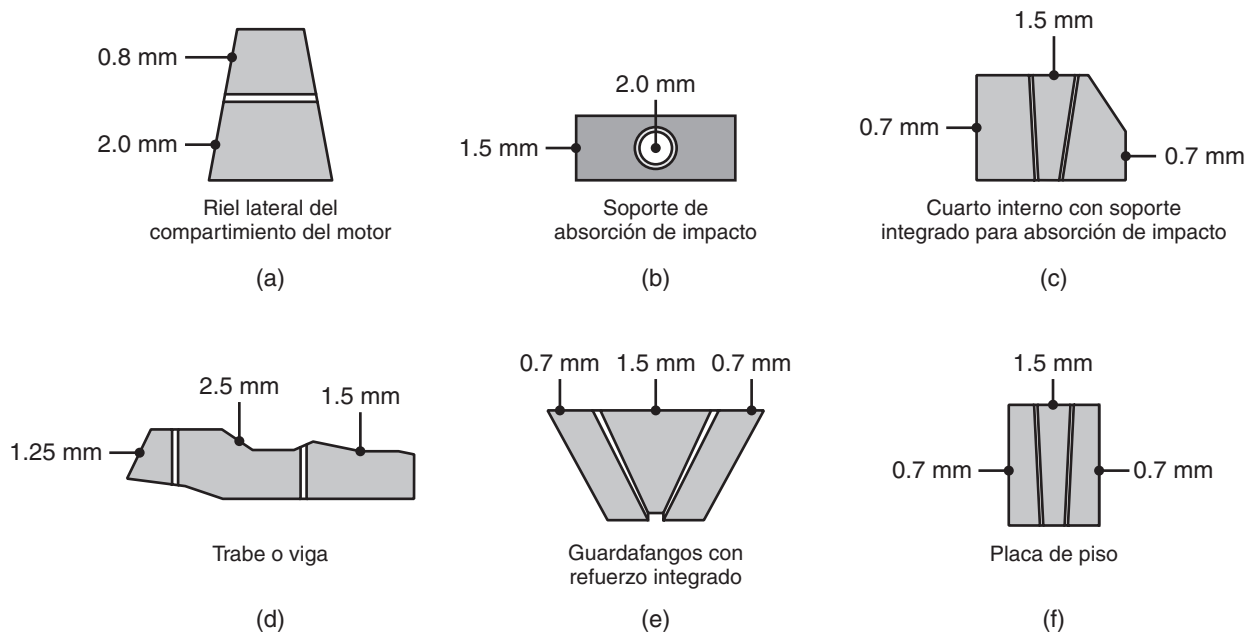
Ejemplos de componentes de carrocería automotriz soldados a tope con rayo láser y estampados. *Fuente:* M. Geiger y T. Nakagawa.
